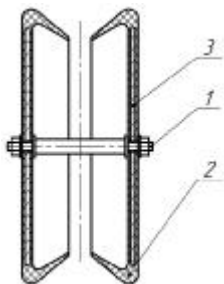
Конструкція вдосконаленого конусного котка: 1 – вісь; 2 – гнучкий гумовий обід; 3 – металевий диск.
